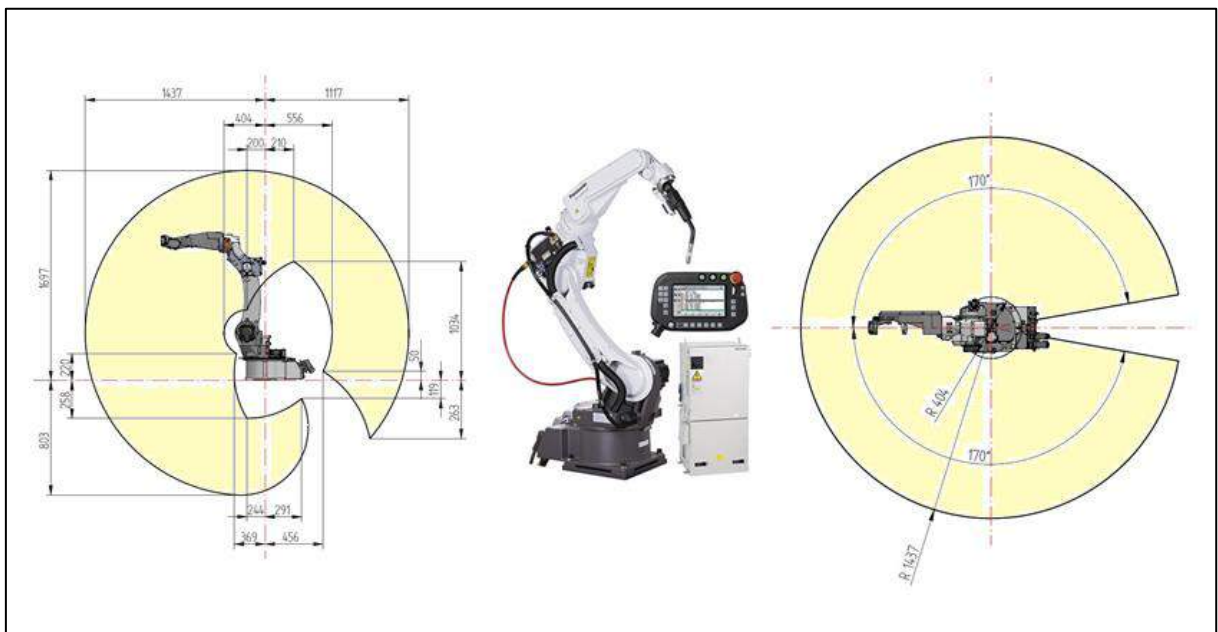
Soldagem com robô, adaptado de POWERMIG, 2016.
